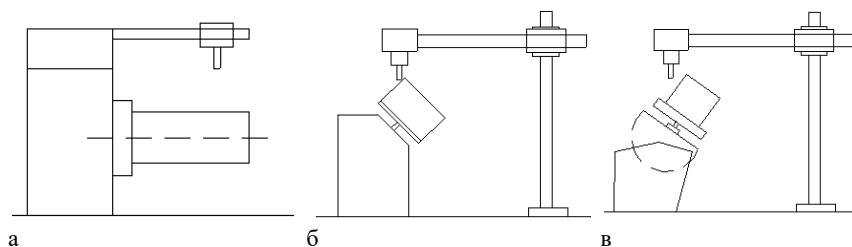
Установки для сварки круговых швов средних и крупных деталей, закреплённых консольно: *а, б* – вращатели с фиксированным углом наклона; *в* – вращатели с переменным углом наклона
